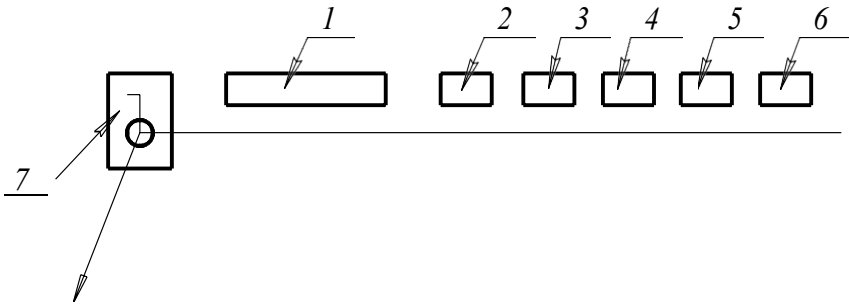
Структура условного обозначения сварного шва
